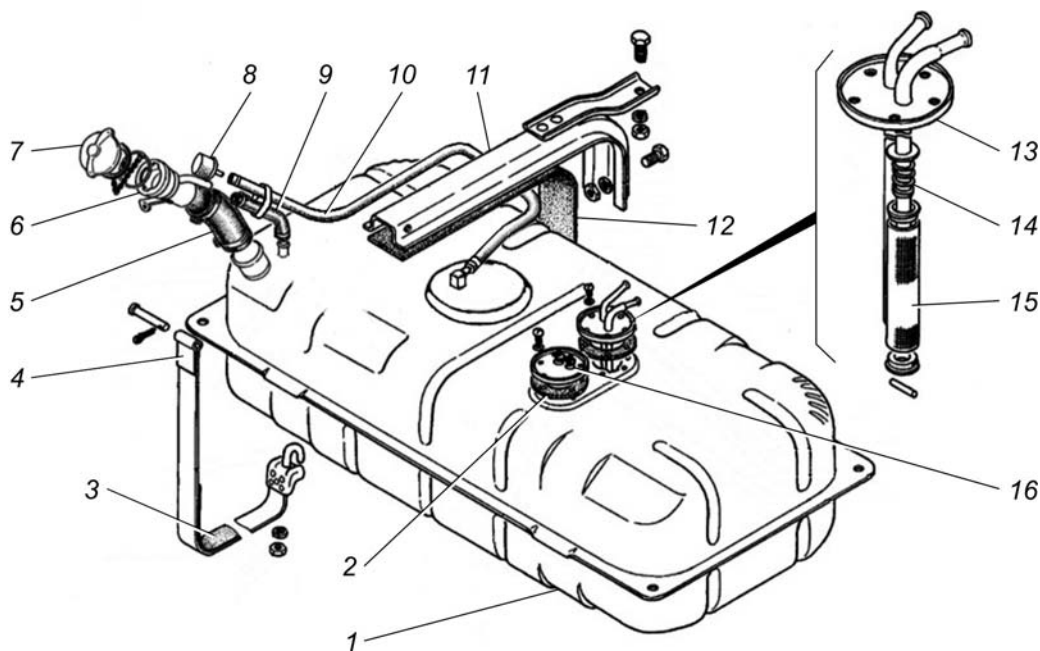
Топливный бак: 1 - бак топливный; 2, 3 и 12 - прокладки; 3 - хомут; 5 - шланг наливной трубы; 6 - труба наливная; 7 - пробка наливной трубы; 8 - клапан давления и разрежения; 9 - шланг воздушной трубки; 10 - шланг клапана давления и разрежения; 11 - кронштейн; 13 - фланец забора и слива топлива; 14 - пружина; 15 - фильтр; 16 - датчик электрического указателя уровня топлива
